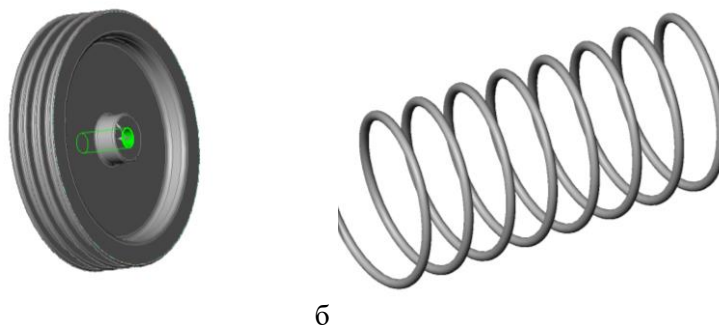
а) шкив для ременной передачи; б) пружина для распорной плиты
